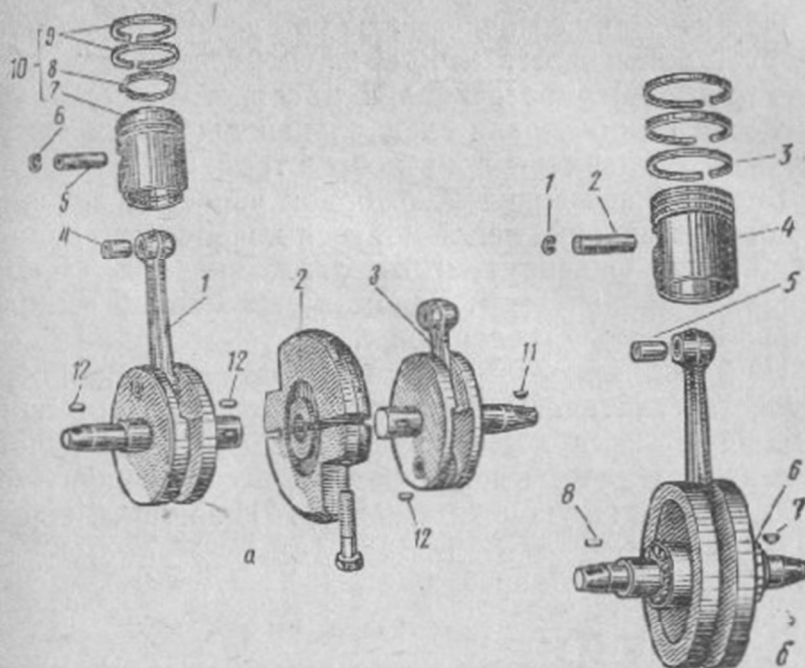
Кривошипно-поршневая группа «Иж-ЮЗ» (а) и детали коленчатого вала «Иж-ПЗ» (б) (позиции даны в табл. 22 и 23)
